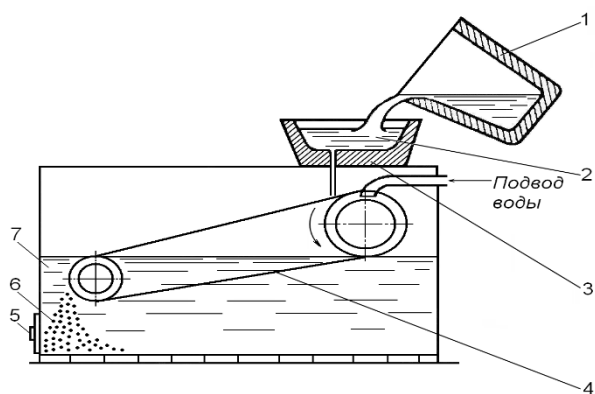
Схема грануляции: 1-ковш; 2- расплавленный металл; 3-промежуточный ковш; 4-лента; 5-разгрузочный люк; 6- порошок; 7-вода
